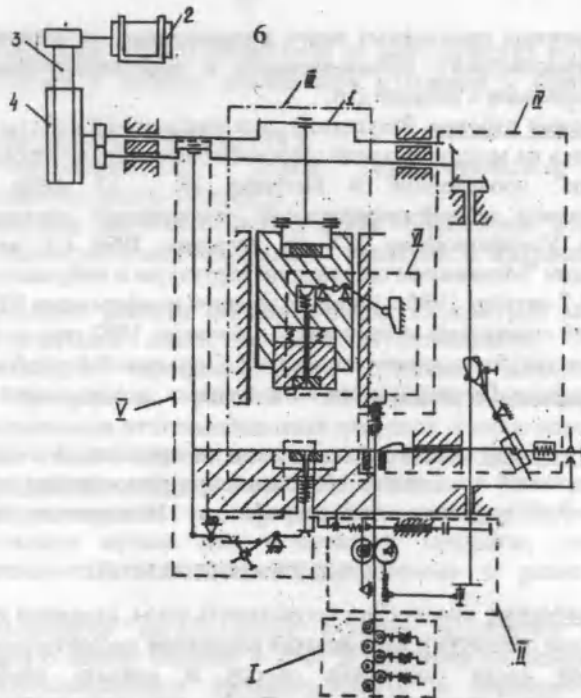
Кинематическая схема шарикоштамповочного пресса-автомата.
